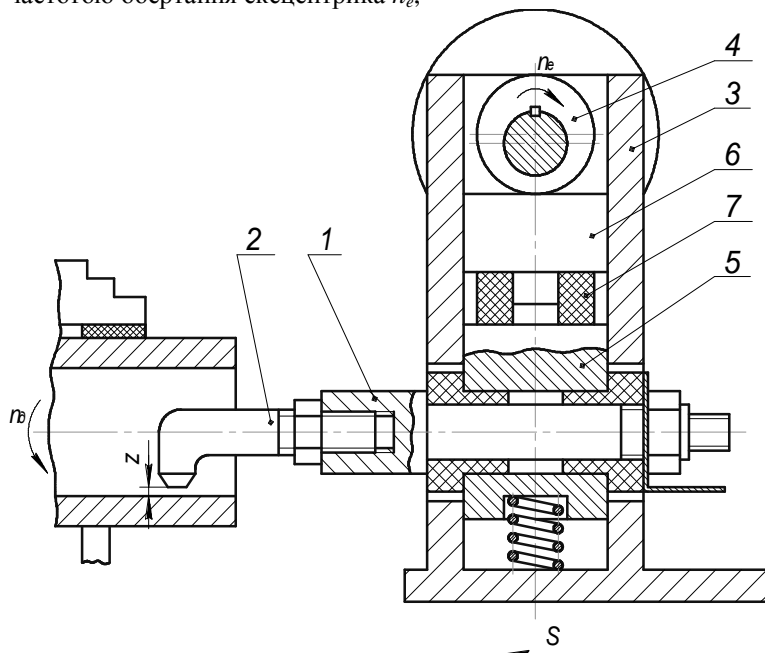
Установка деталі і пристрій з жорсткою штангою для електроконтактної дискретної обробки внутрішньої поверхні
